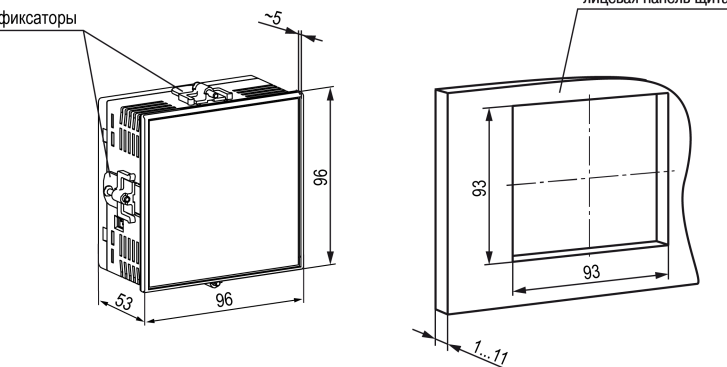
Габаритные размеры корпуса Щ1 и монтажного отверстия в щите
